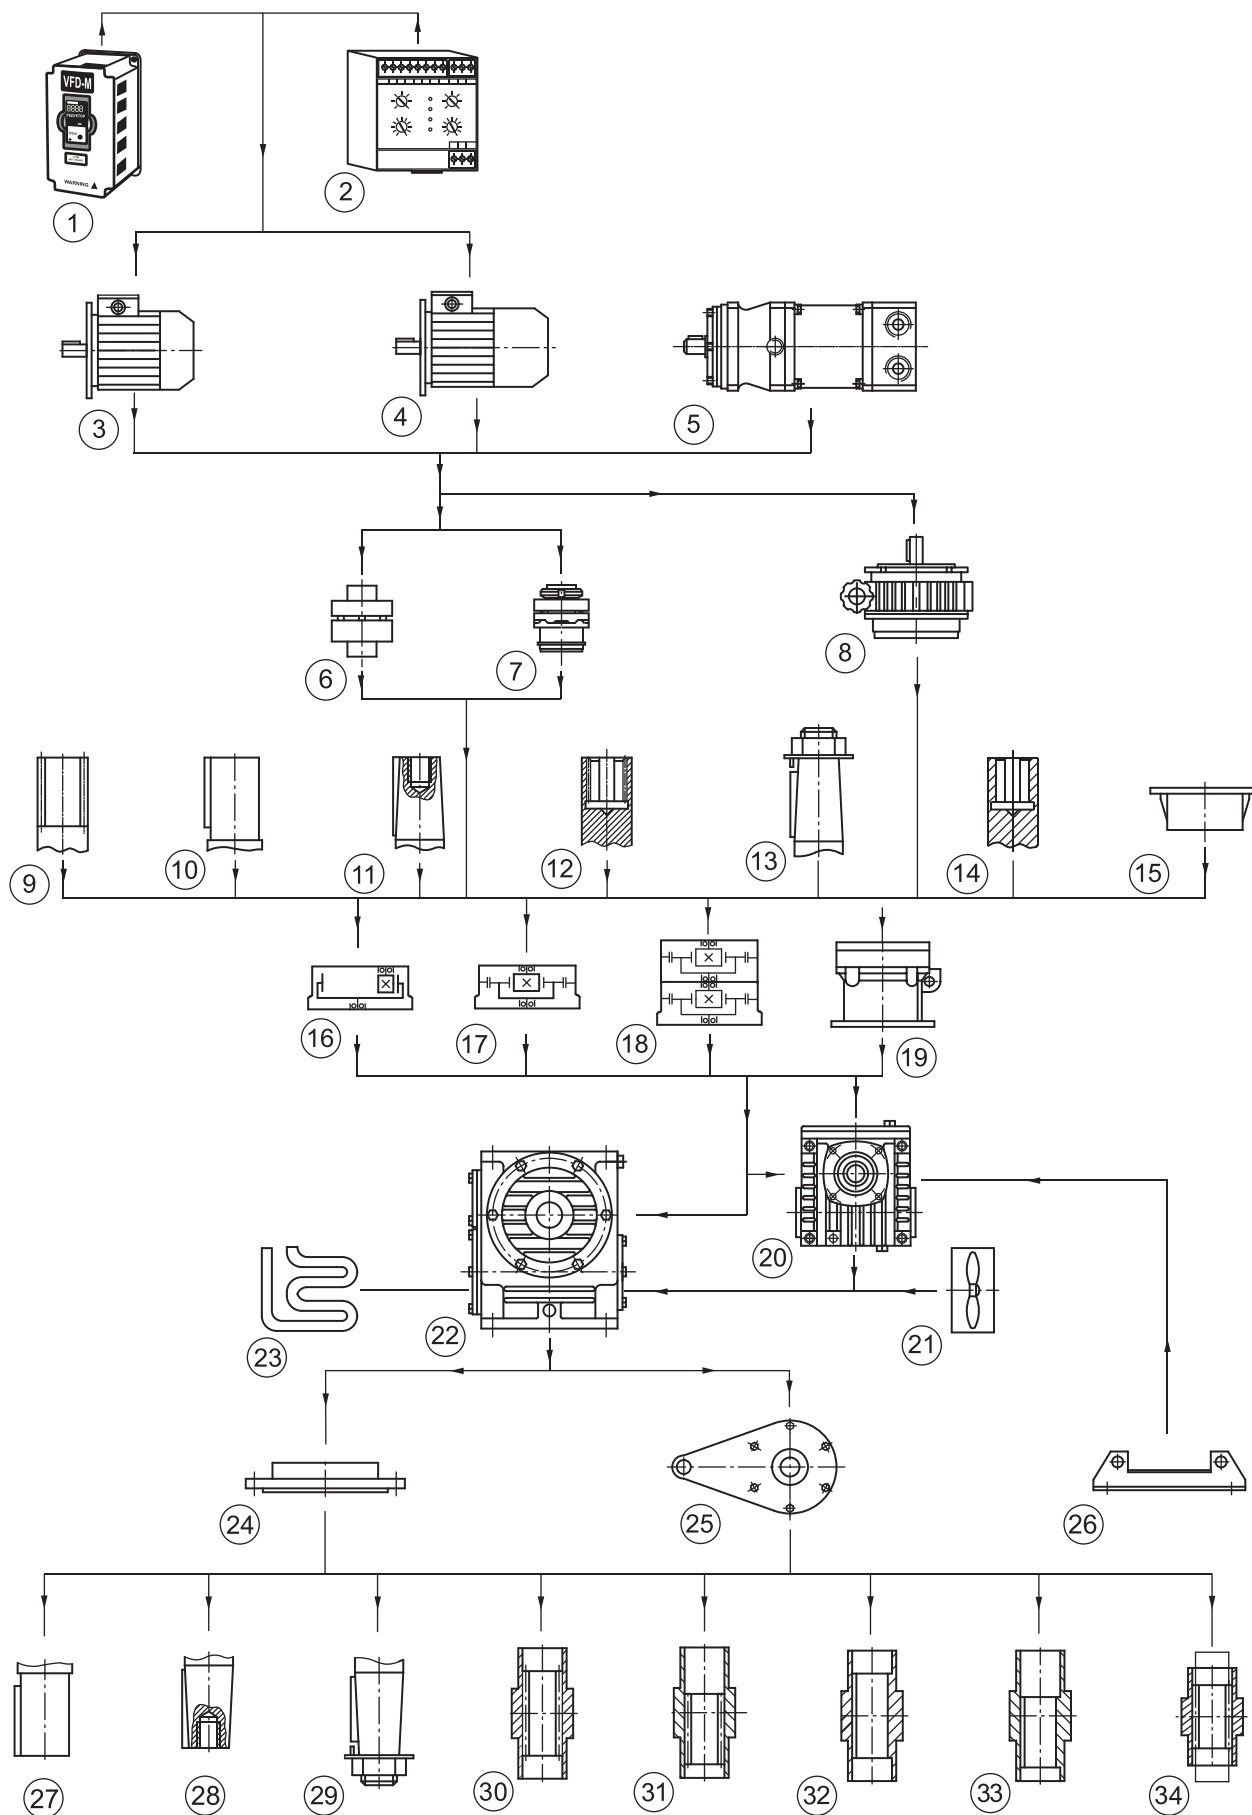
Блочно-модульная схема построения червячных, цилиндро-червячных и планетарно-червячных редукторов и мотор-редукторов:
